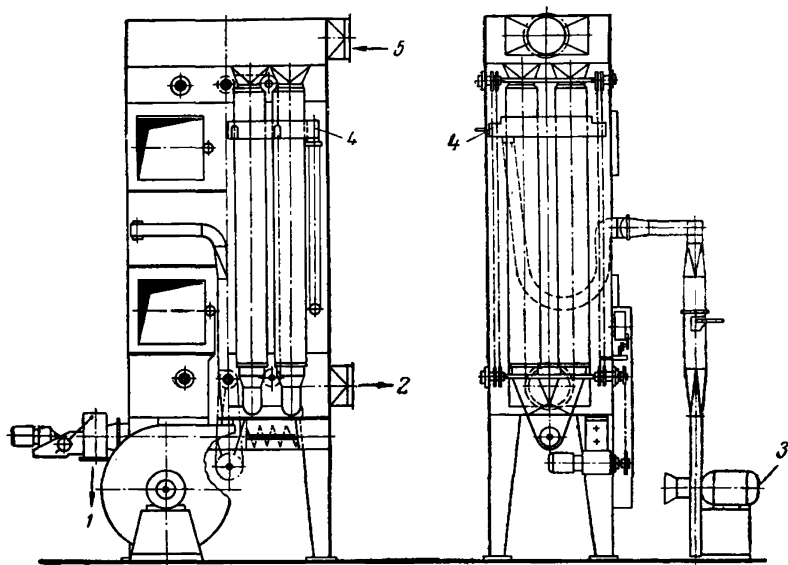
Вертикальный многорукавный фильтр; очистка реверсированием струи:
